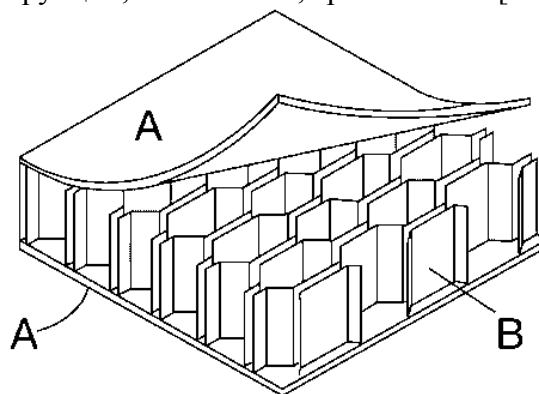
Общий вид трехслойной конструкции: А – несущие слои; В – наполнитель.
